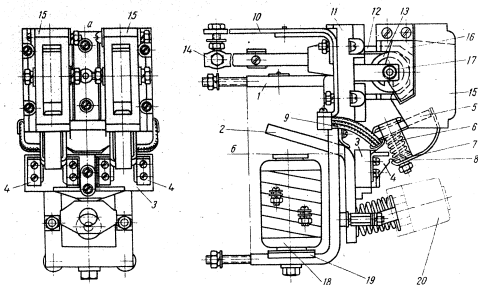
Конструкция контакторов серии КТП 500 с двумя полюсами. 1 — скоба магнитопровода; 2 — якорь; 3 — пластмассовая колодка; 4 — кронштейн; 5 — подвижный контакт; 6 — контактная пружина; 7 — фасонный болт; 8 — рог подвижного контакта; 9 — гибкое соединение; 10, 11 — основные выходы; 11 — основание из пластмассы; 12 — неподвижный контакт; 13 — дугогасительная катушка; 14 — дугогасительная камера; 15 — дугогасительная шайба; 16 — сердечник дугогасительной катушки; 17 — дугогасительная катушка; 18 — дугогасительная катушка; 19 — дугогасительная катушка; 20 — блокконтакты
